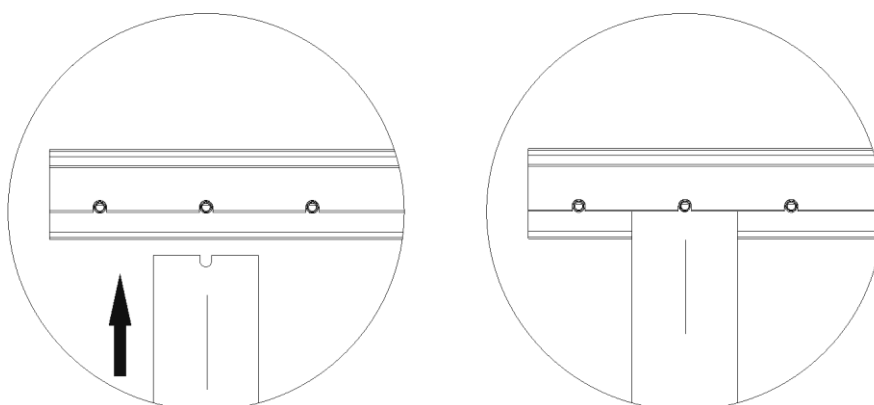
Einsetzen des mono Connector Boards, exemplarisch
